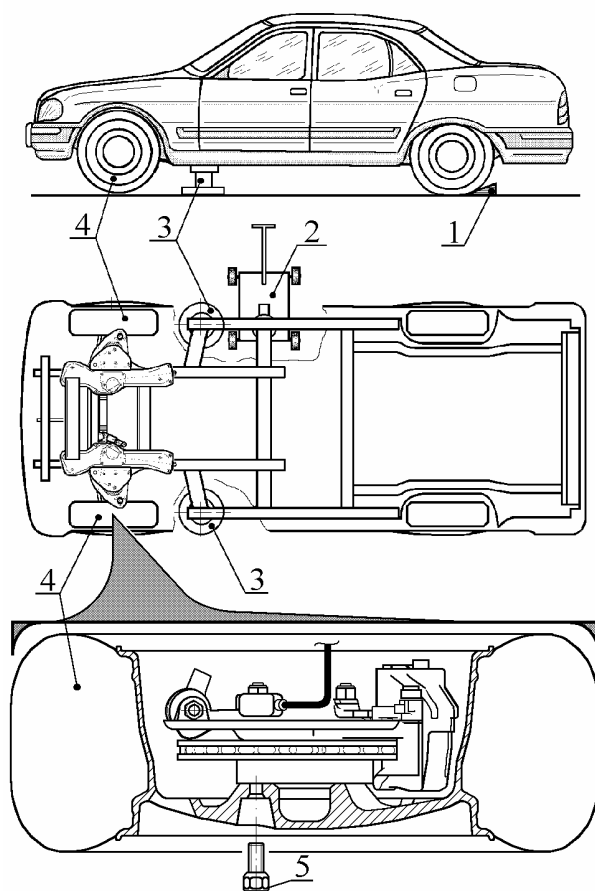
Установка подставок под автомобиль и снятие передних колес:
